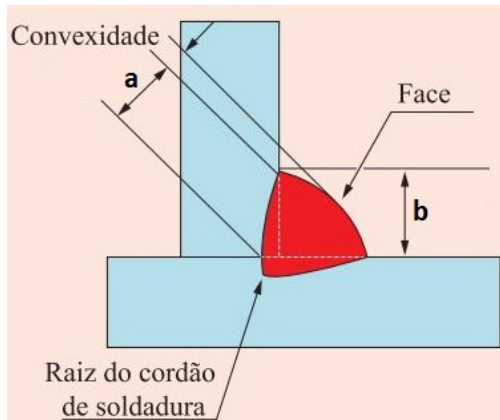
Nomenclatura da geometria dos cordões de soldadura (adaptado de Silva, 2016).
